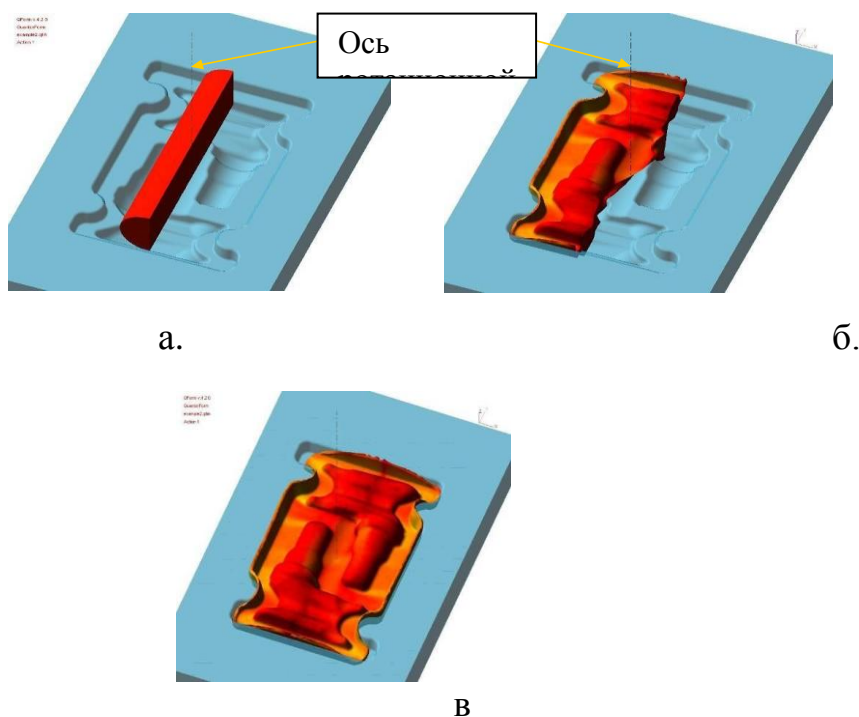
Ротационная симметрия первого типа имеет место, если из одной заготовки штампуются две одинаковые поковки. При расчете использована половина заготовки
